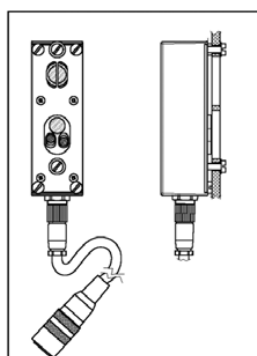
Sensore con cavo innestabile. Sensor with cable engaged.
